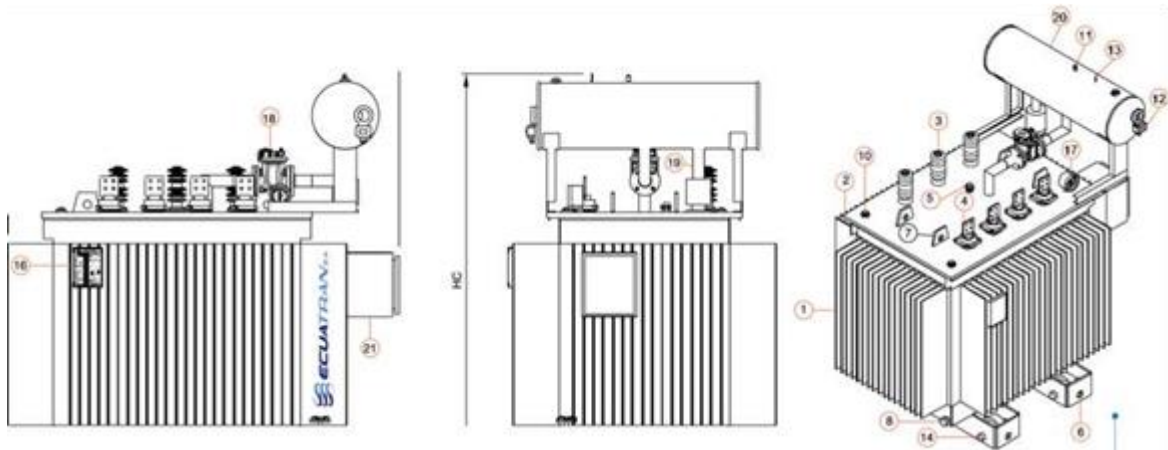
Partes de un transformador trifásico subestación con tanque de expansión desde 500 -1000 KVA
